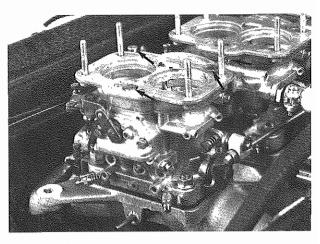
Viti fissaggio coperchio carburatore Carburettor cover fixing screws
